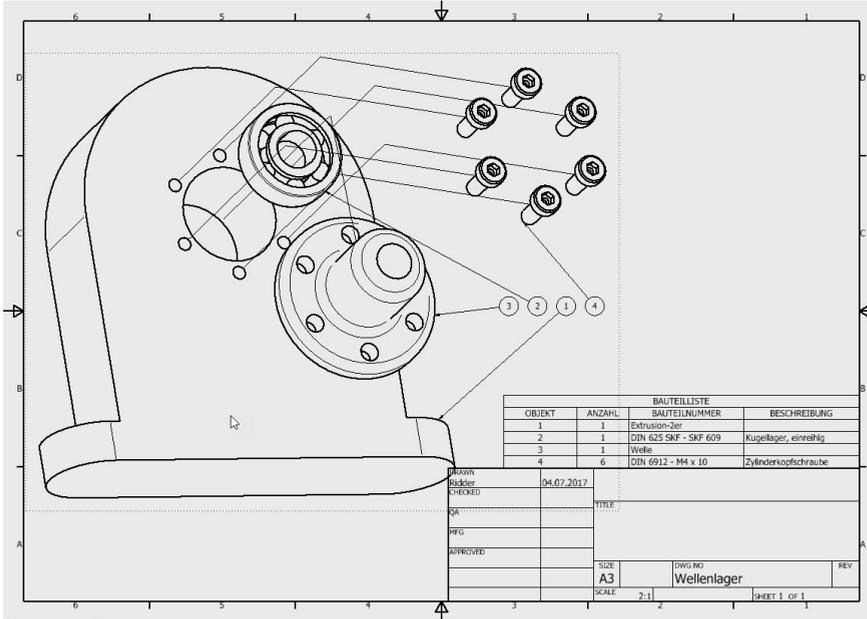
Zeichnung der Explosionsansicht mit Positionsnummern und Stückliste
